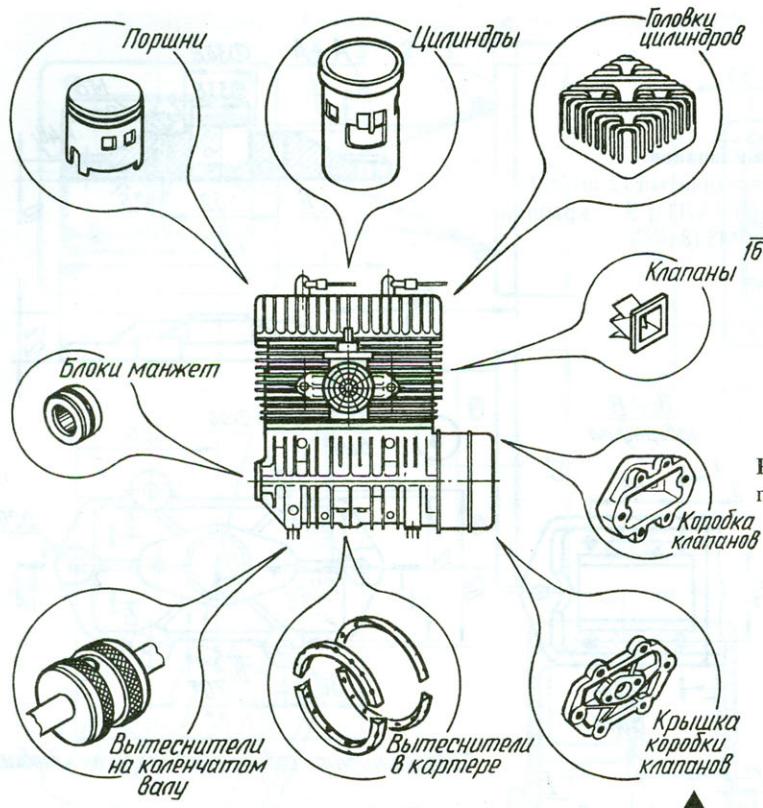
Узлы и детали серийного двигателя РМЗ-640 «Буран», которые были вновь изготовлены или модернизированы.
